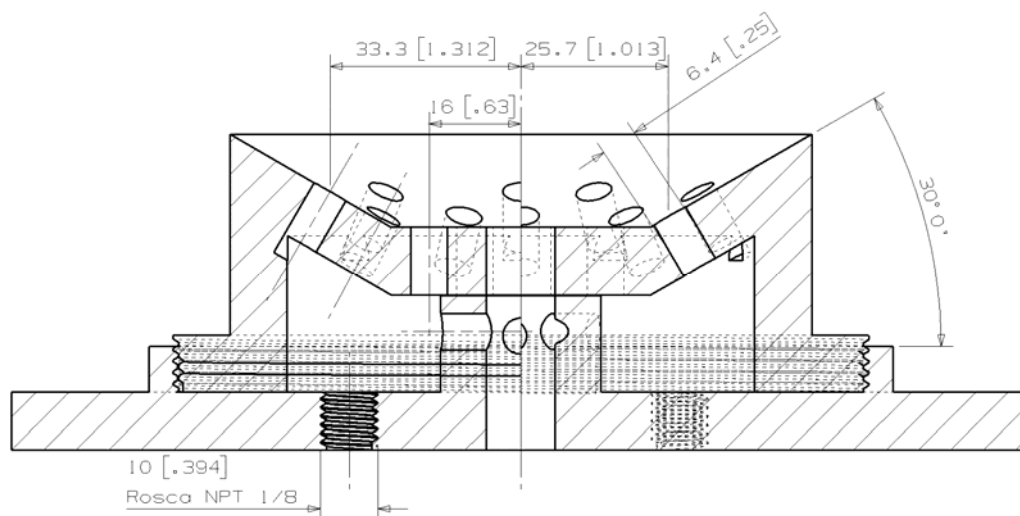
Parte estática del cojinete neumático. Dimensiones en mm [plg].
